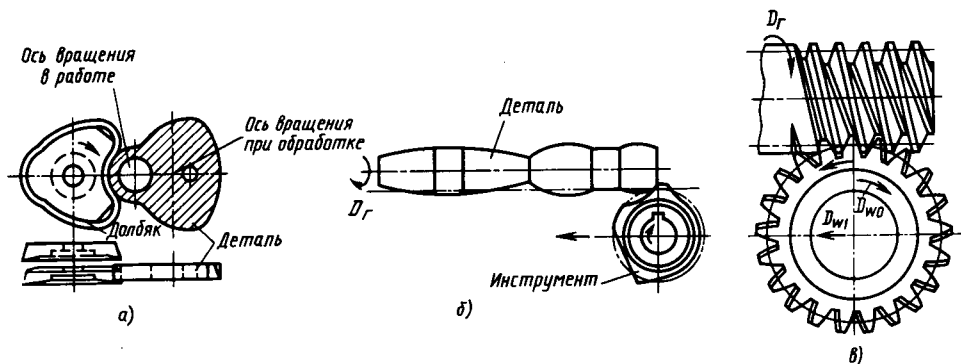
Долбяк и обкатные резцы для изготовления фасонных профилей деталей
